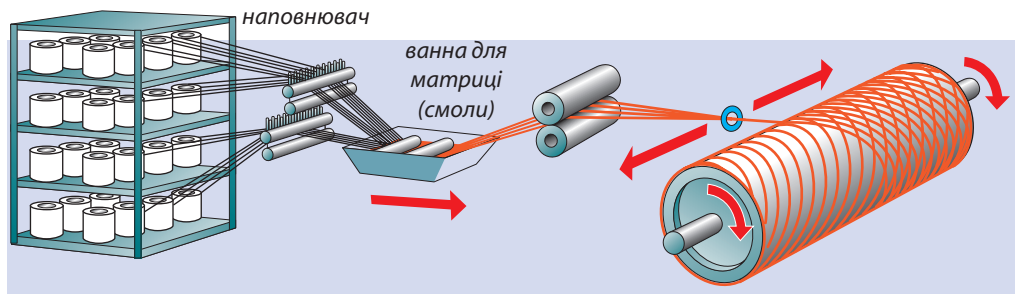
Виготовлення виробу з композиту способом намотування
